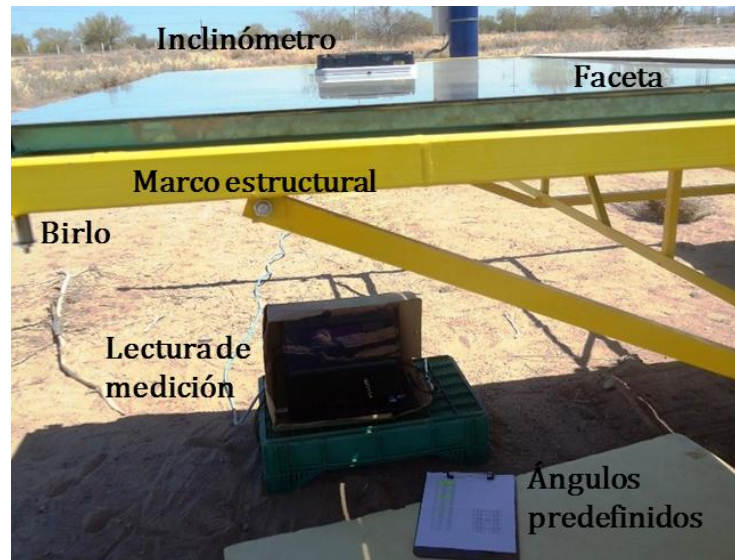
Arreglo para el pre canteo de facetas en piso.
